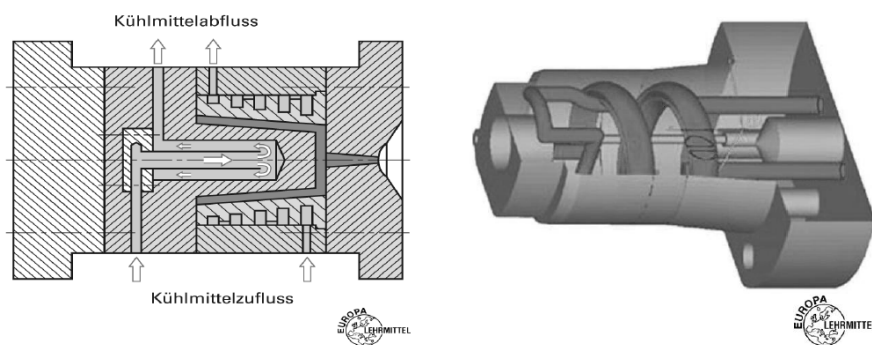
Aufbau des Werkzeugs mit Kühlmitteldurchlauf
